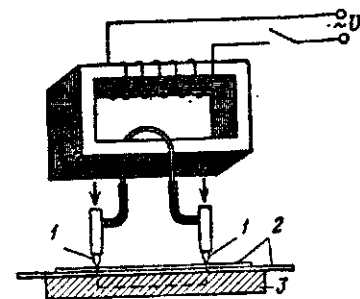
Схема устройства для односторонней двухточечной сварки: 1 — электроды; 2 — свариваемые детали; 3 — подкладка
